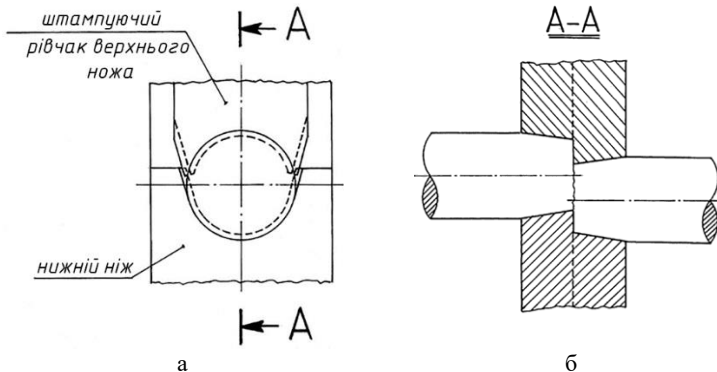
Схема різання профільними ножами зі штампом виступами (а), розріз по А-А (б).
